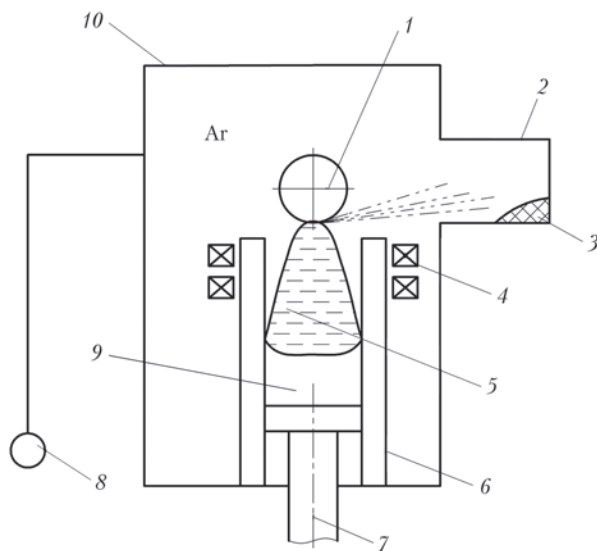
Процесс диспергирования: 1 — закалочный диск; 2 — бункер; 3 — чешуйки; 4 — индуктор; 5 — расплавленная ванна металла; 6 — секционный кристаллизатор; 7 — поддон; 8 — вакуумный насос; 9 — переплавляемая заготовка; 10 — камера
